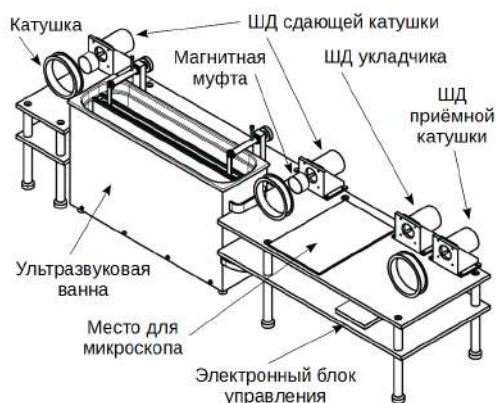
Общий вид нового перемоточного станка с возможностью ультразвуковой мойки. ШД — шаговый двигатель.
